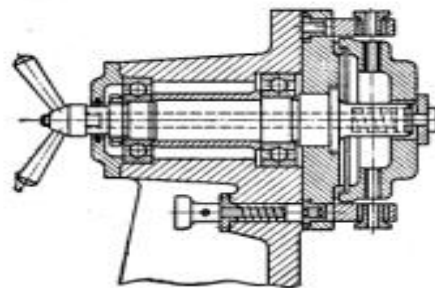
Поворотний кондуктор для свердлувального верстата
